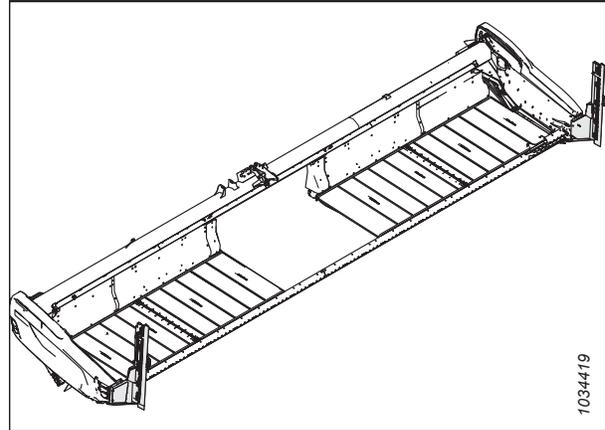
kits du couteau vertical VertiBlade^{MC}
